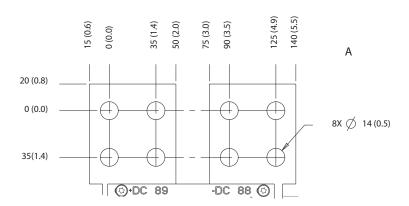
Dimensões dos terminais de regeneração/divisão da carga do E4h
